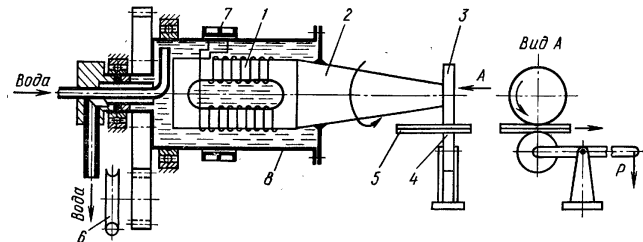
Схема установки для роликовой сварки ультразвуком:
